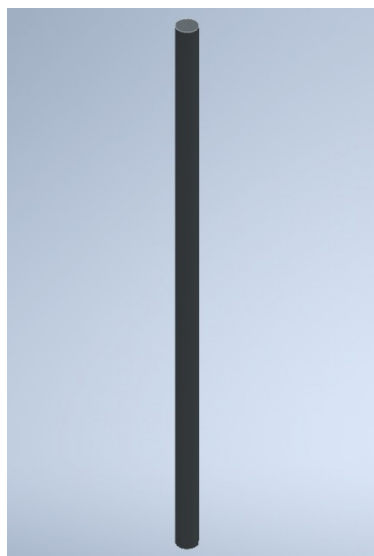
Perspectiva axonométrica de la barra unión de engranajes.
